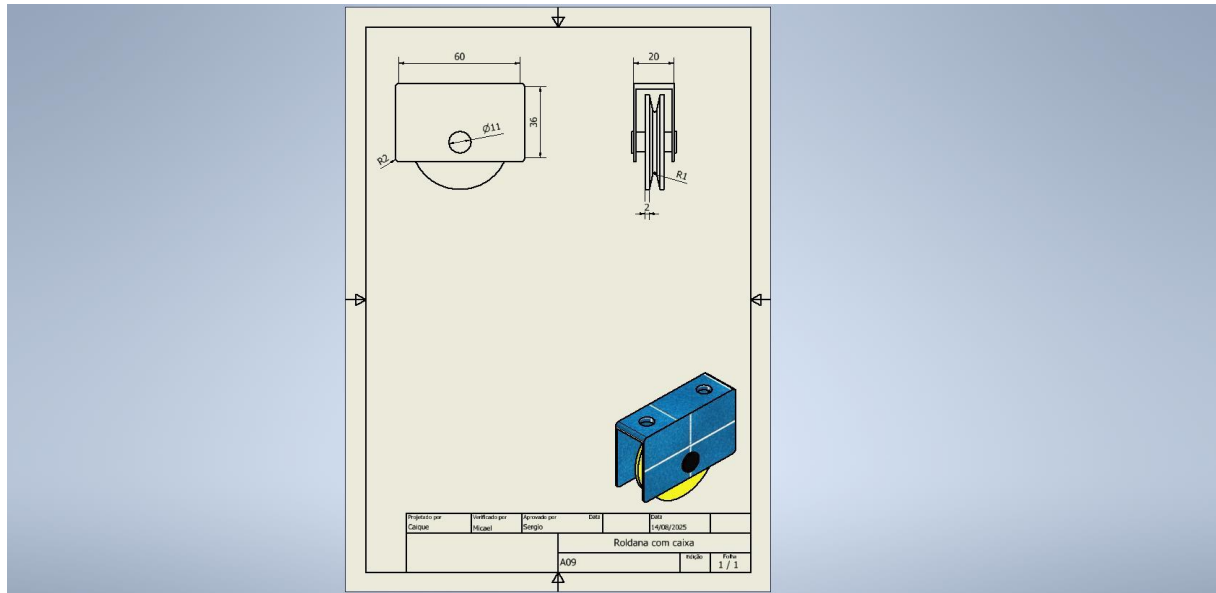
1- Desenho da Roldana do suporte do cabo de Aço - Fonte - Caique Piaia- Inventor
